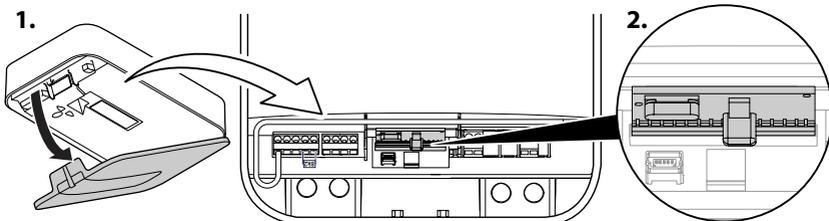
Aprire il coperchio della testata del motore e definire il modulo radio.
